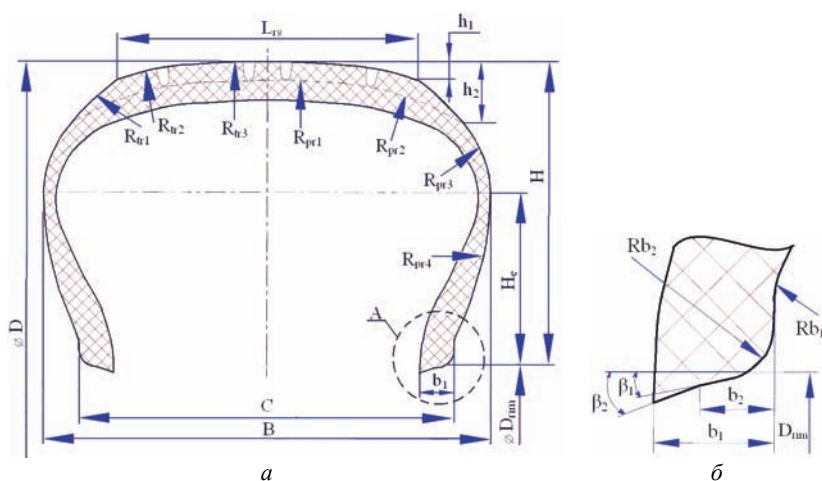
Геометрическая модель профиля поперечного сечения пневматической шины и его основные размеры: а – профиль шины; б – борт
